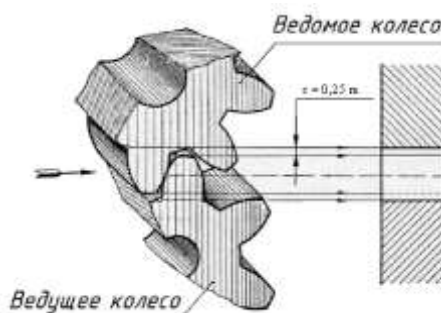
Радиальный зазор зубчатой передачи
